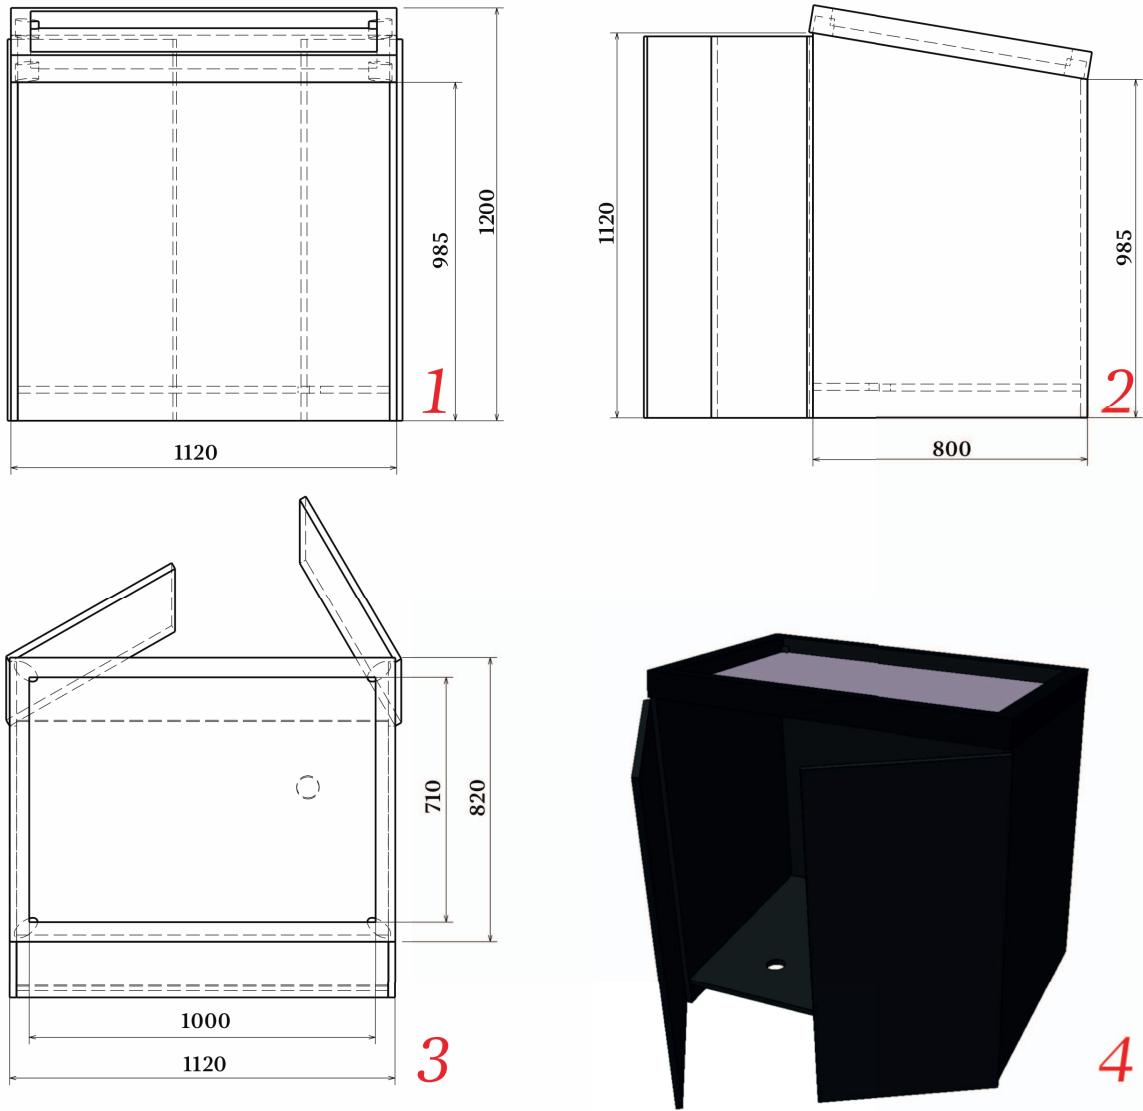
CAD Zeichnung des Jean-Pierre Aufbaus
